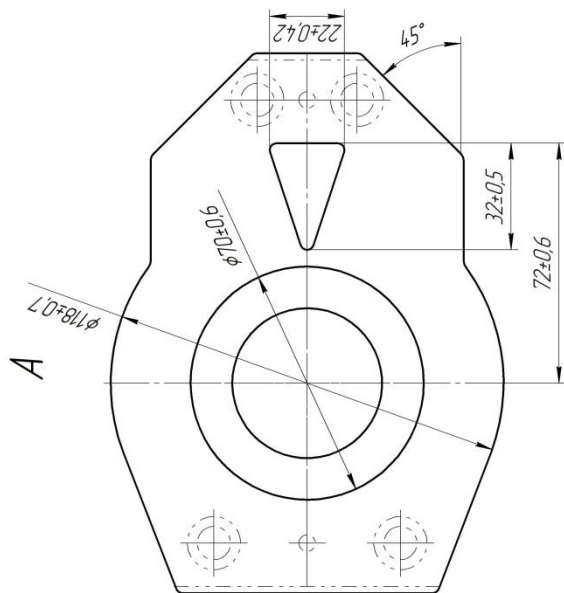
Общий вид заготовки - «Крышка лебедки»
